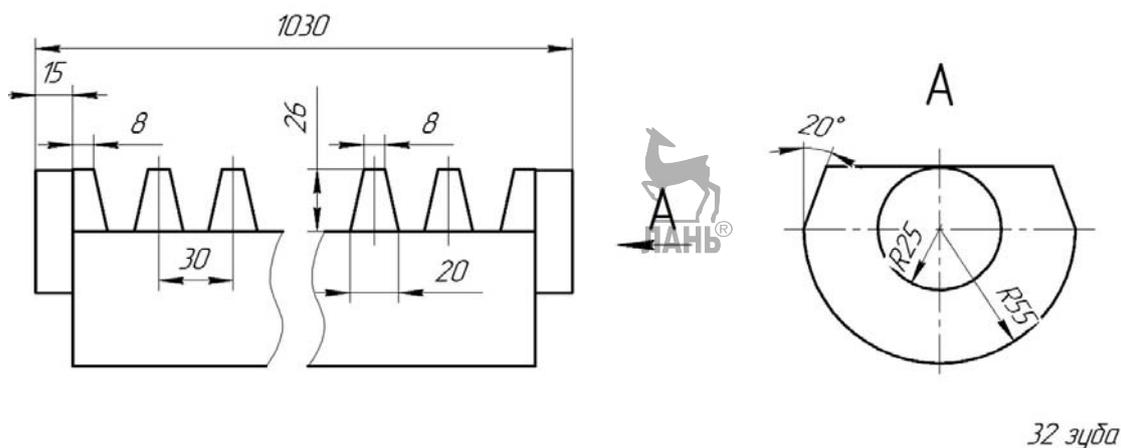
Чертеж шток-рейки корпуса ОПУ
